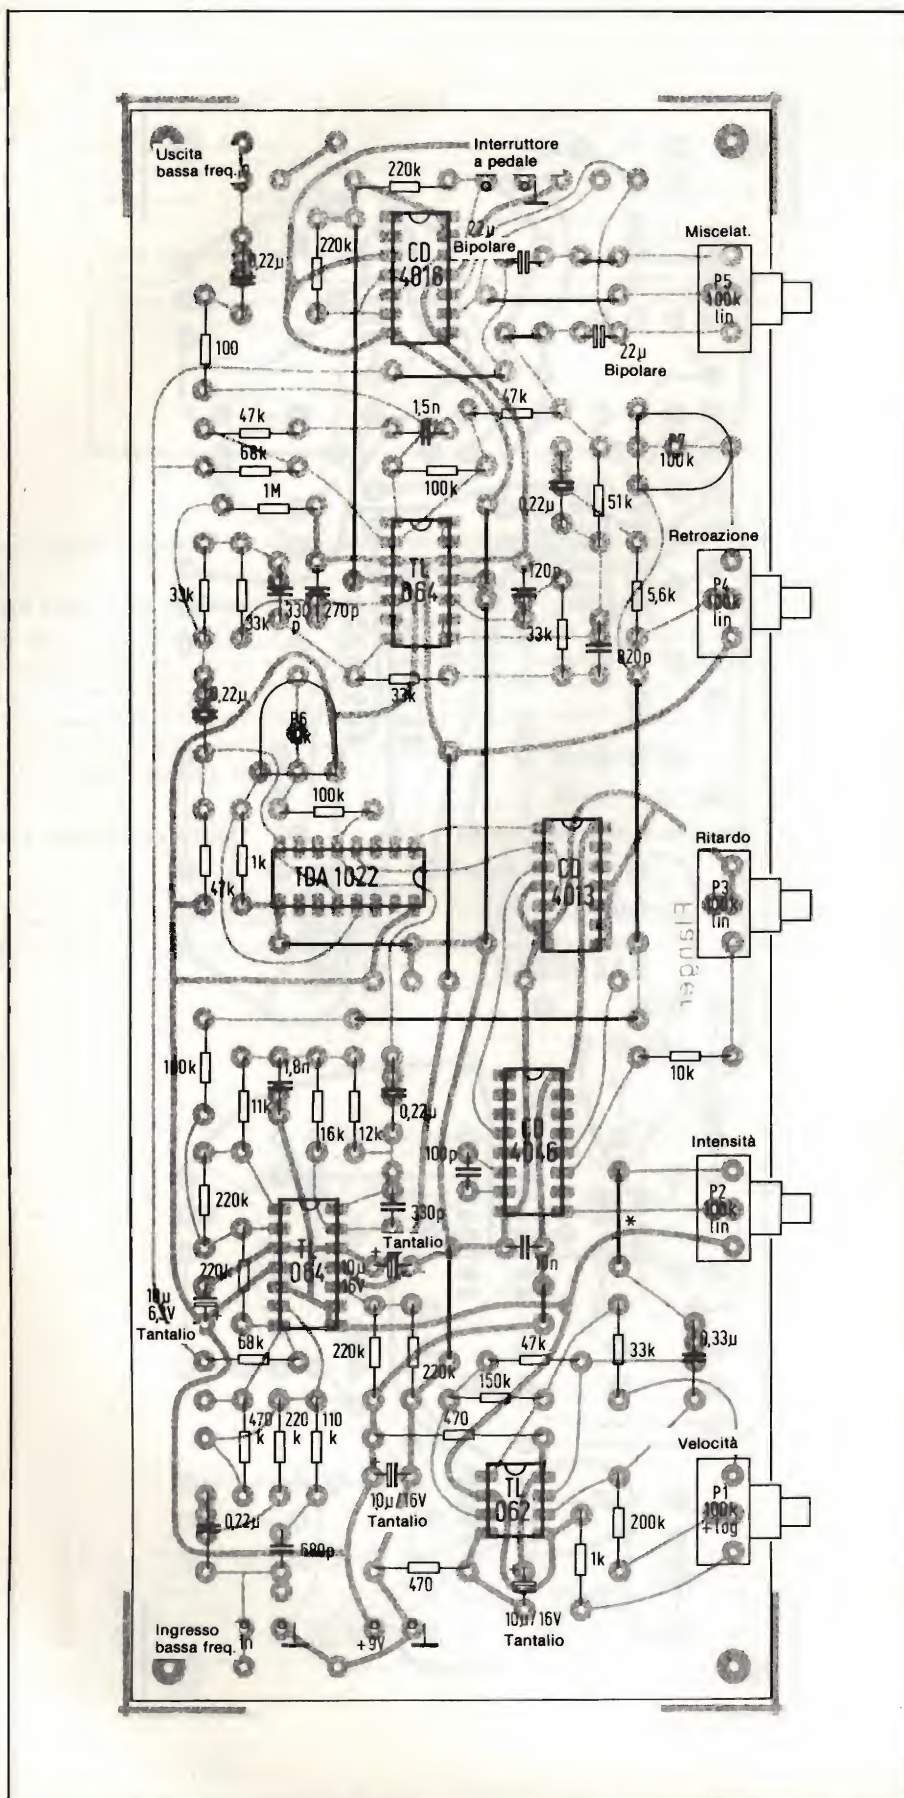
Anche i potenziometri di regolazione sono direttamente montati sul circuito stampato, come illustrato su questo disegno della disposizione dei componenti. Durante la costruzione dovranno essere osservati i suggerimenti contenuti nel testo.
